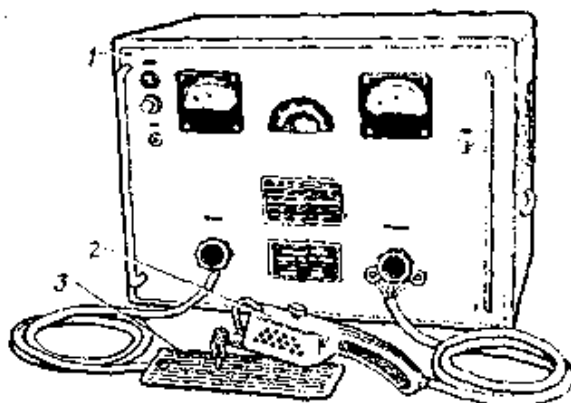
Зовнішній вигляд установки ЕФИ-10
